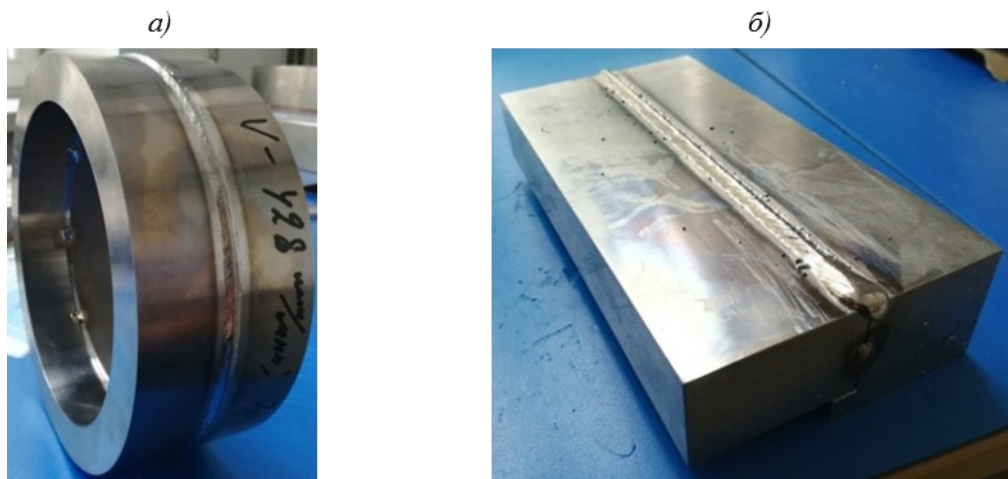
Полуфабрикаты из сплава VT22M после сварки:
